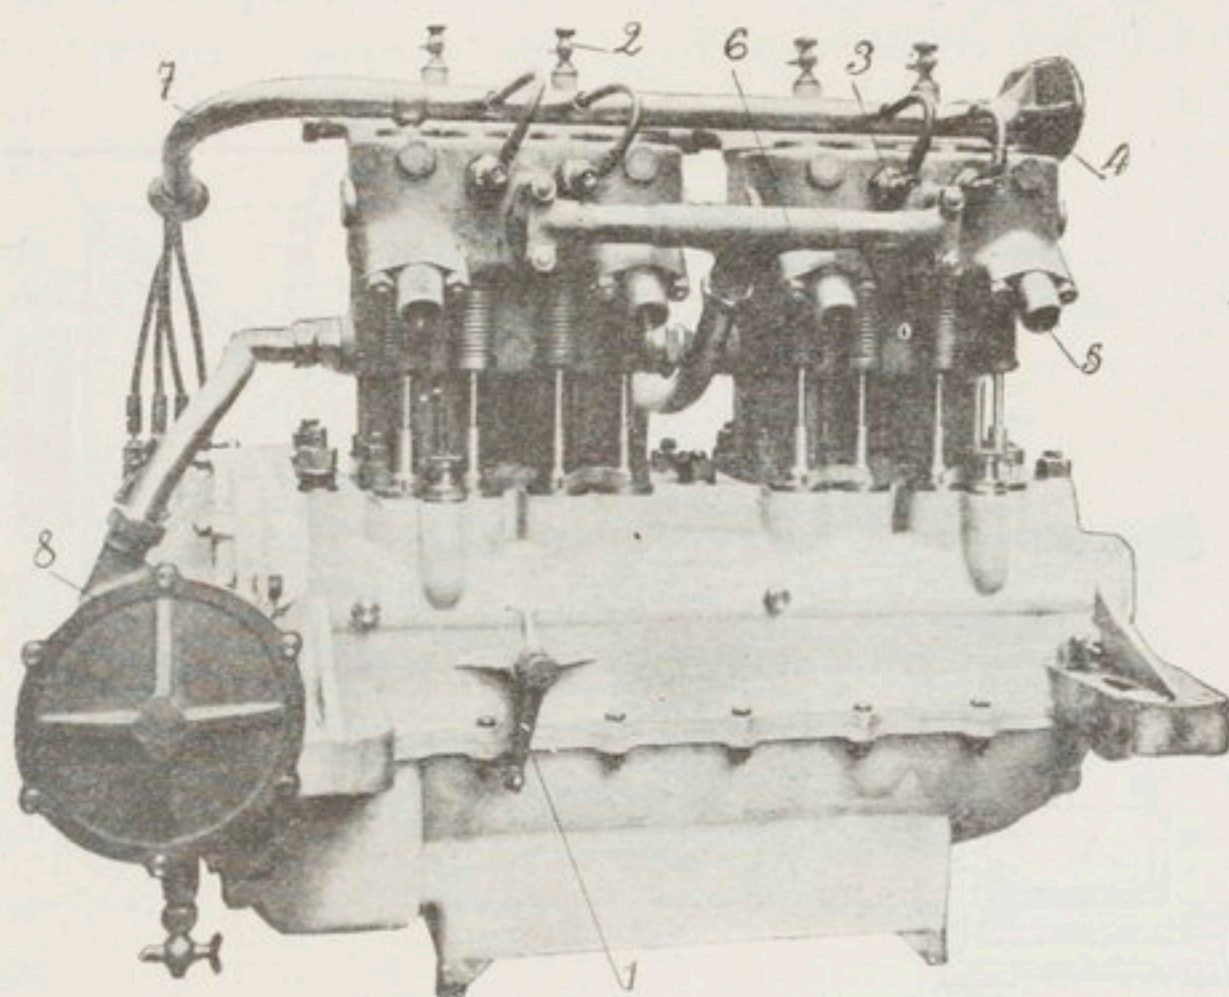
Vue d'ensemble du moteur d'automobile à quatre cylindres de Dion-Bouton.
